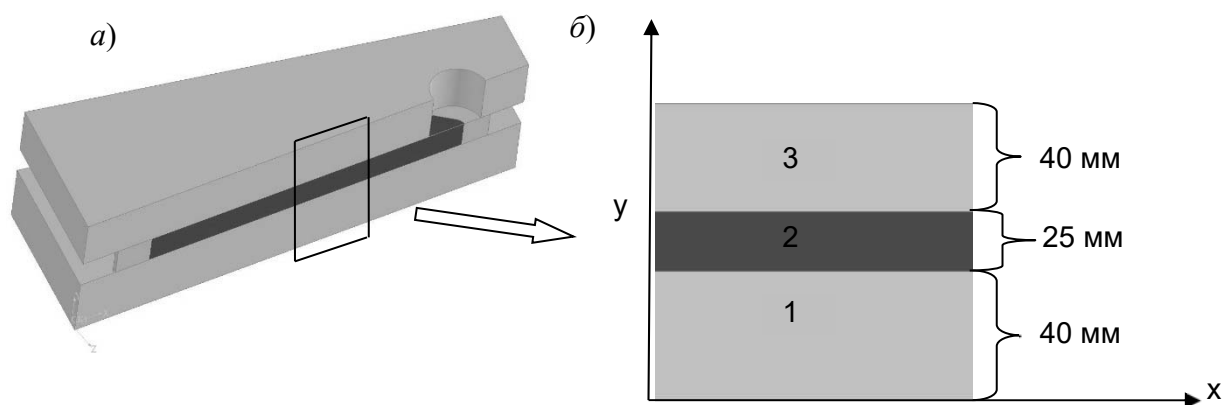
Выбор расчётной области (б) в сечении сборки (а) отливки и формы: 1, 3 – форма; 2 – ИЧХ
